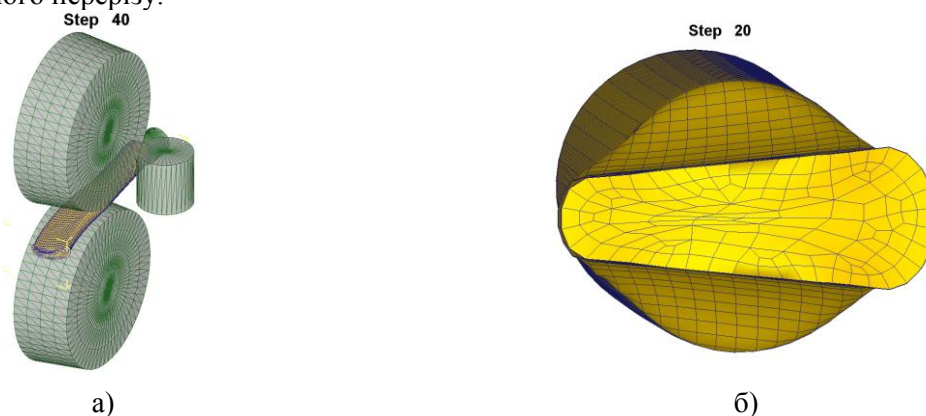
Схема вальцювання заготовки конічними валками а) та форма поперечного перетину вальцюваної ділянки б)
